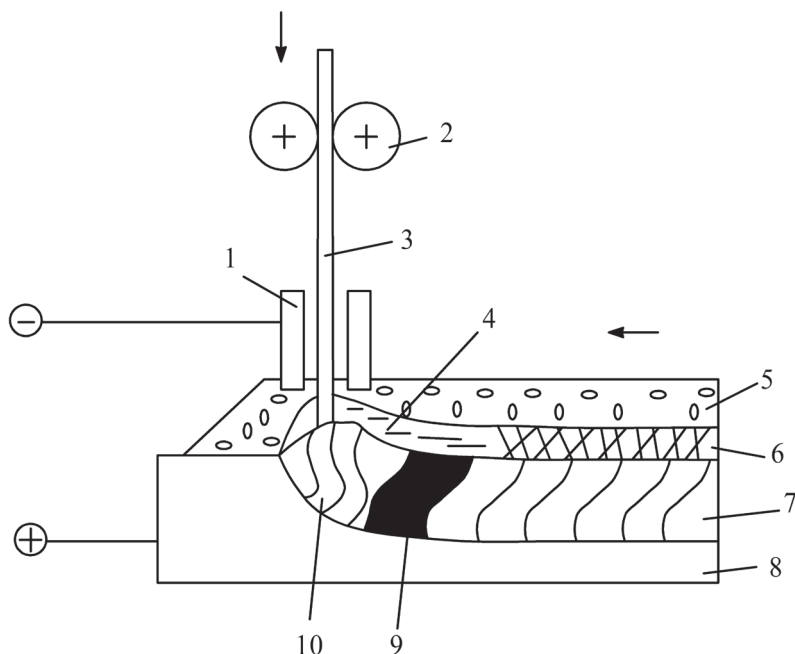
Схема дуговой сварки под флюсом:
